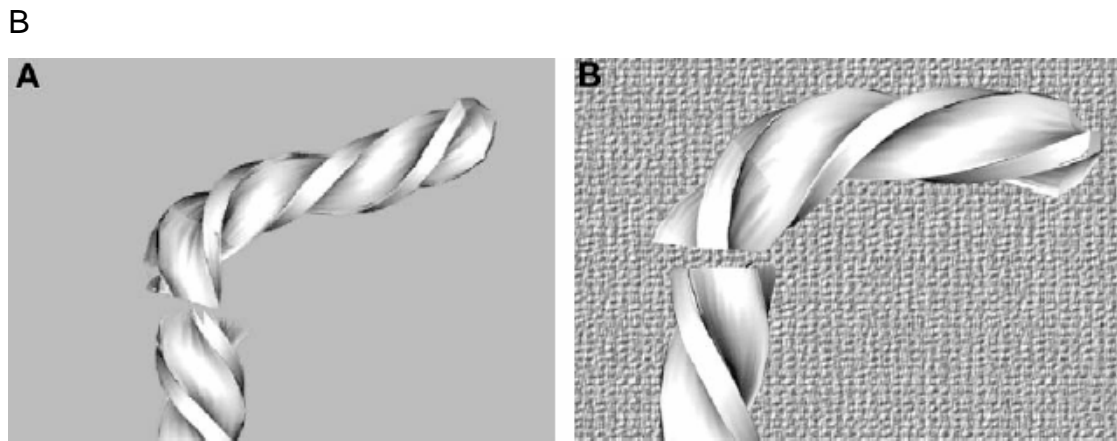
A Fractura torsional, B fractura Flexional. M. K. Iqbal, Dental Clinics, Am 48, 2004
